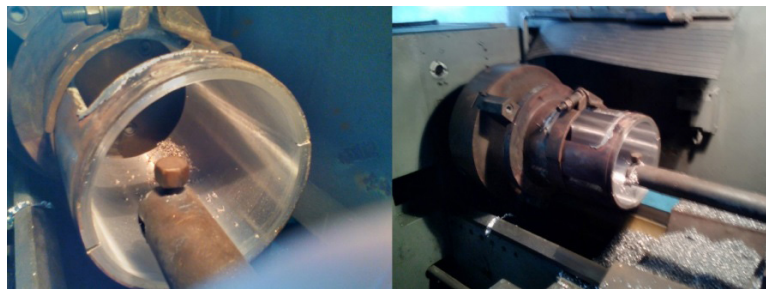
Обточка на токарно-винторезном станке моторно-осевого подшипника электровоза
